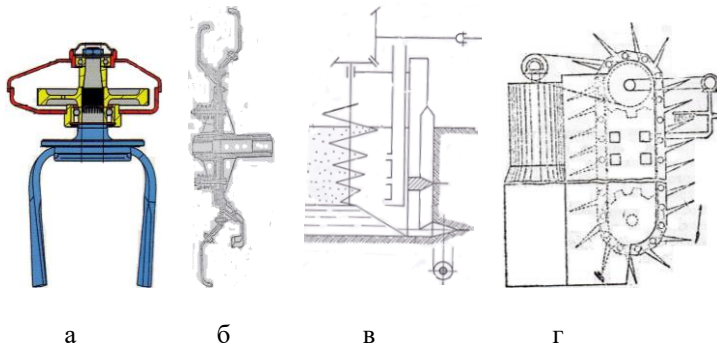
Активні робочі органи лісосадильних машин: а – фрезерний з вертикальною віссю обертання; б – фрезерний з горизонтальною віссю обертання [5]; в – шнековий [4]; г – скребковий робочий орган [6]
